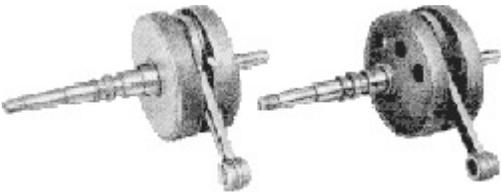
Kurbelwelle ES 250 neue Ausführung (links), alte Ausführung (rechts)
